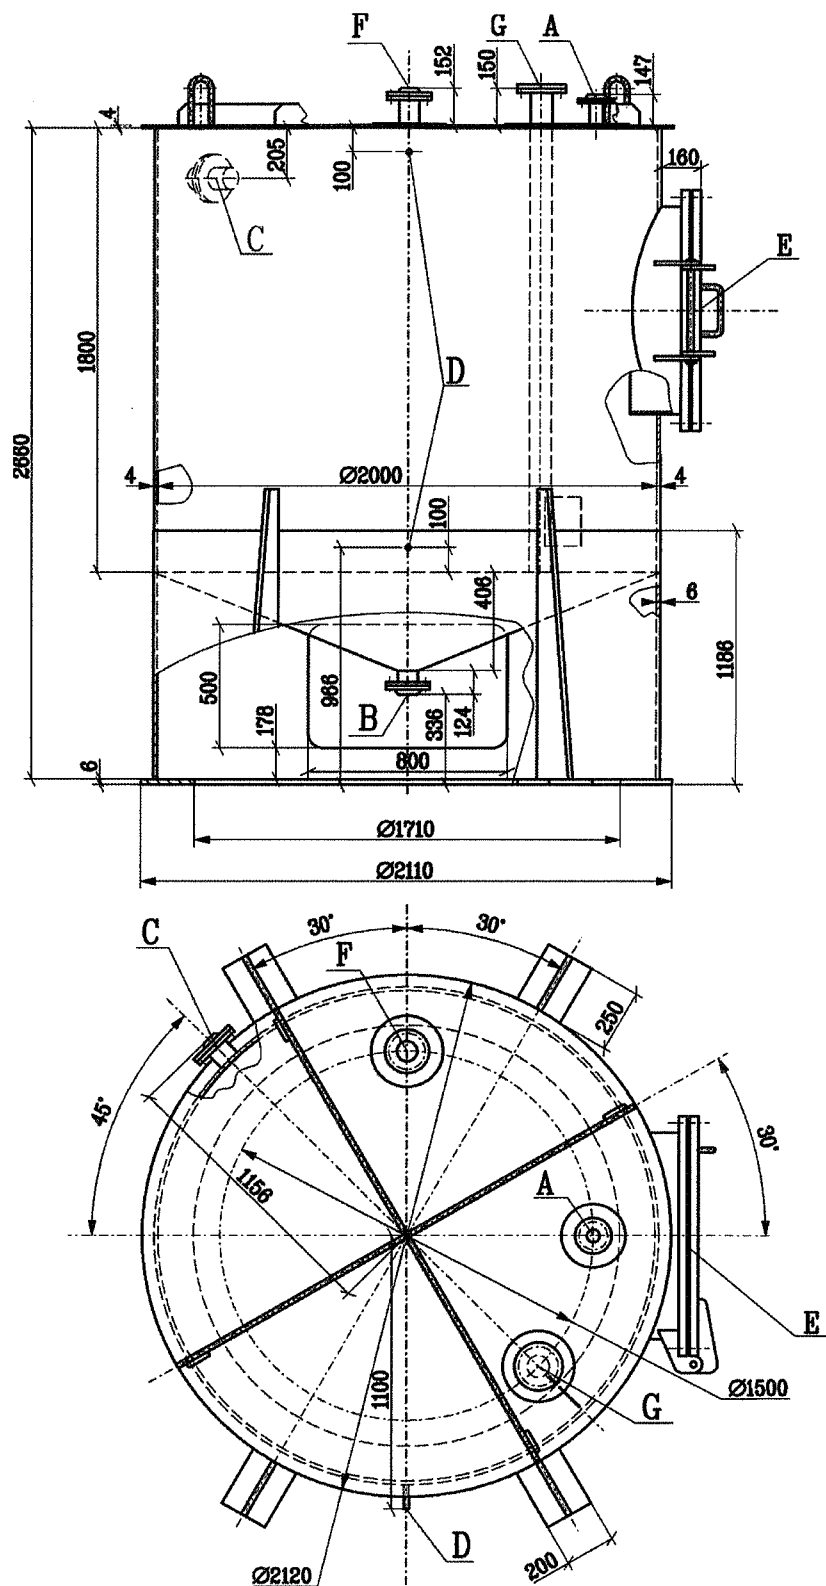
Габаритный чертеж мерника крепкой щелочи LDP20BB001, LDP20BB002
